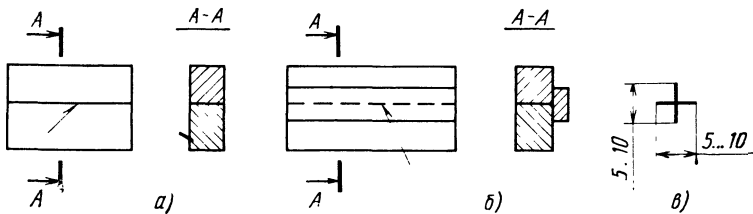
Обозначение сварных швов: видимого (а) и невидимого (б); обозначение и размеры точечного шва (в)
